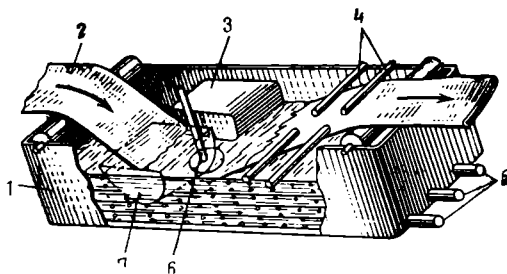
Устройство для опудривания камерной трубки с наружной поверхности:
